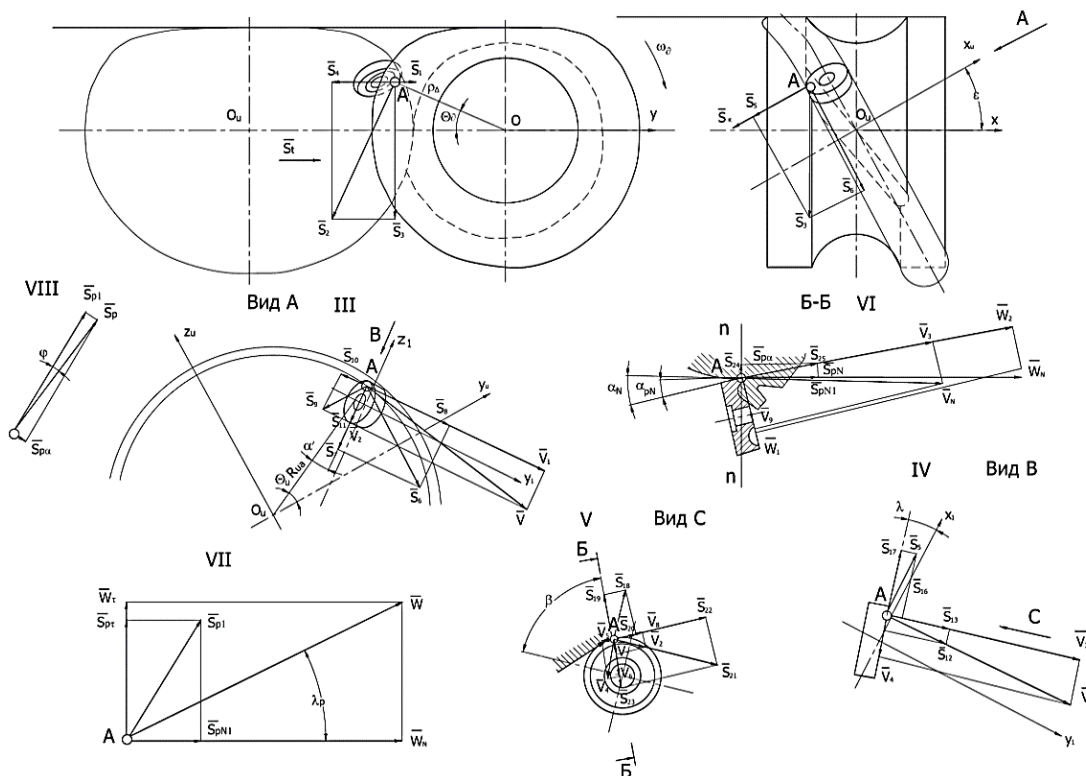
Схема до визначення товщини зрізаного шару і робочих кутів ріжучої частини при обробці зовнішніх торових поверхонь
